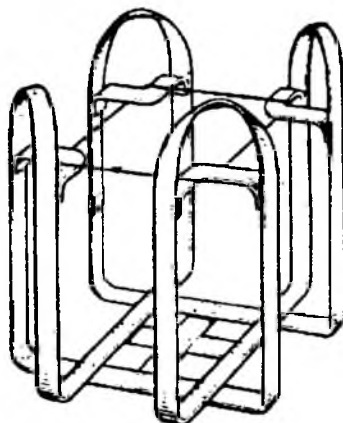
Общий вид четырехветвевового пакетобразующего стропа.
